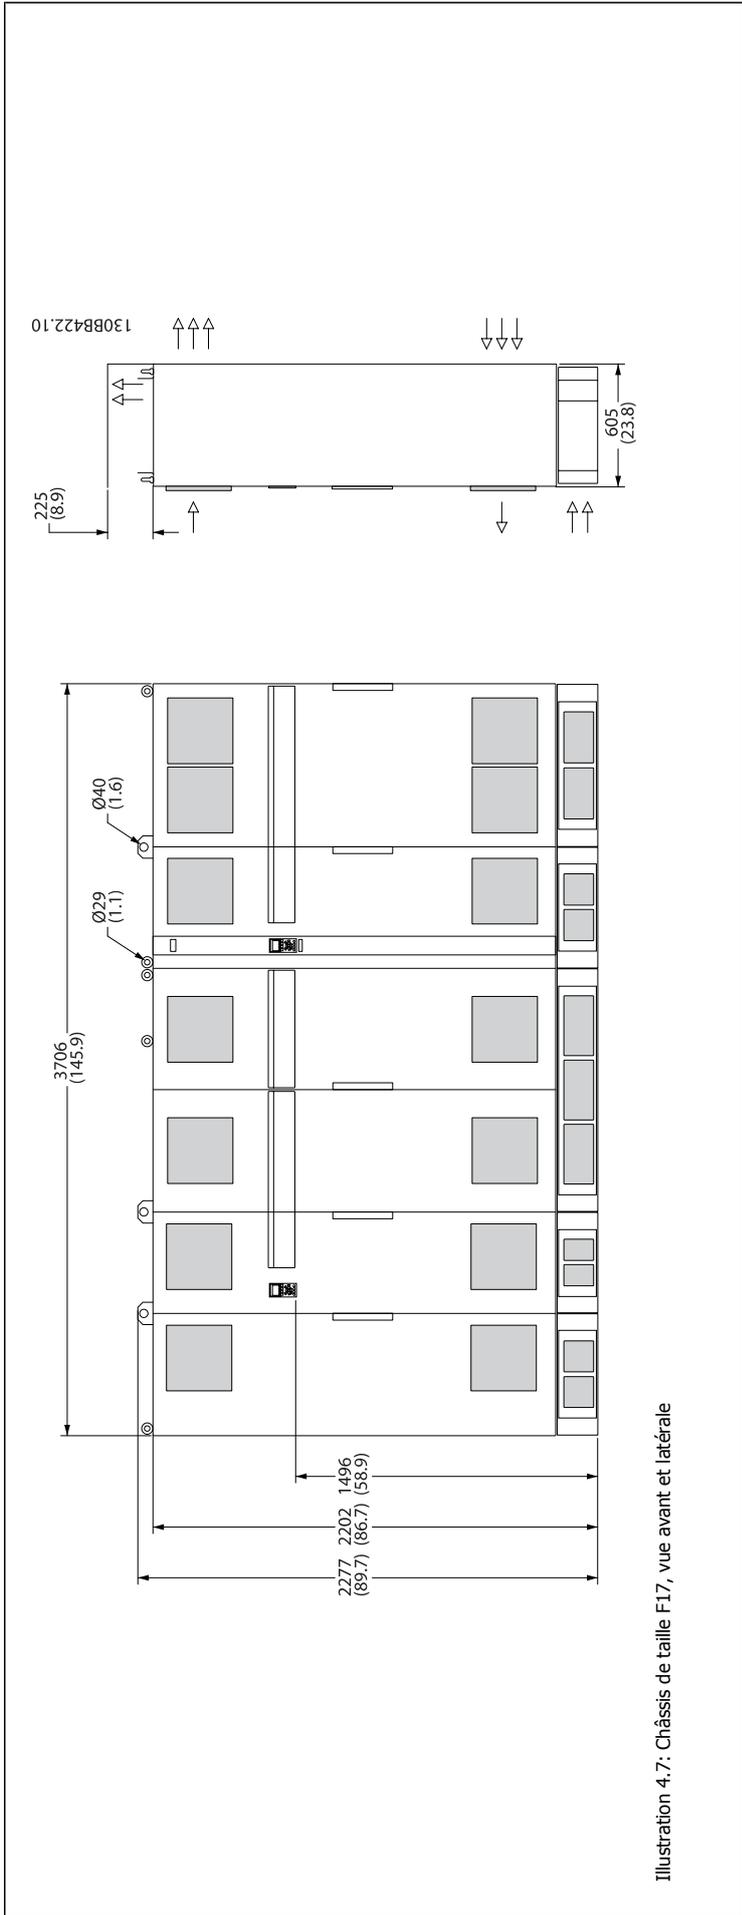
Châssis de taille F17, vue avant et latérale
